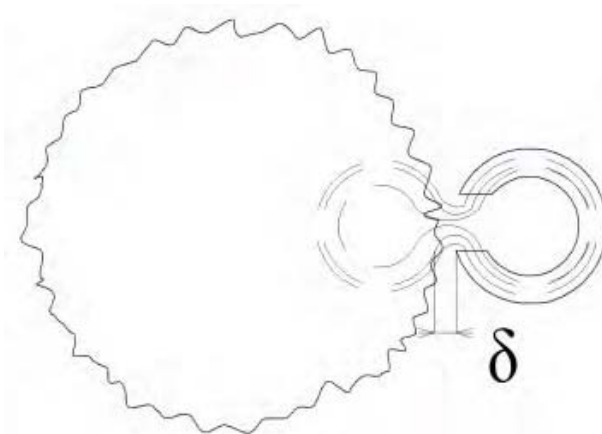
Магнитный поток в цепи головка-зазор-деталь: δ – ширина зазора между магнитной головкой (от катушечного магнитофона - немагнитный зазор – 1 мкм, индуктивность головки - 100 мГн) и деталью
